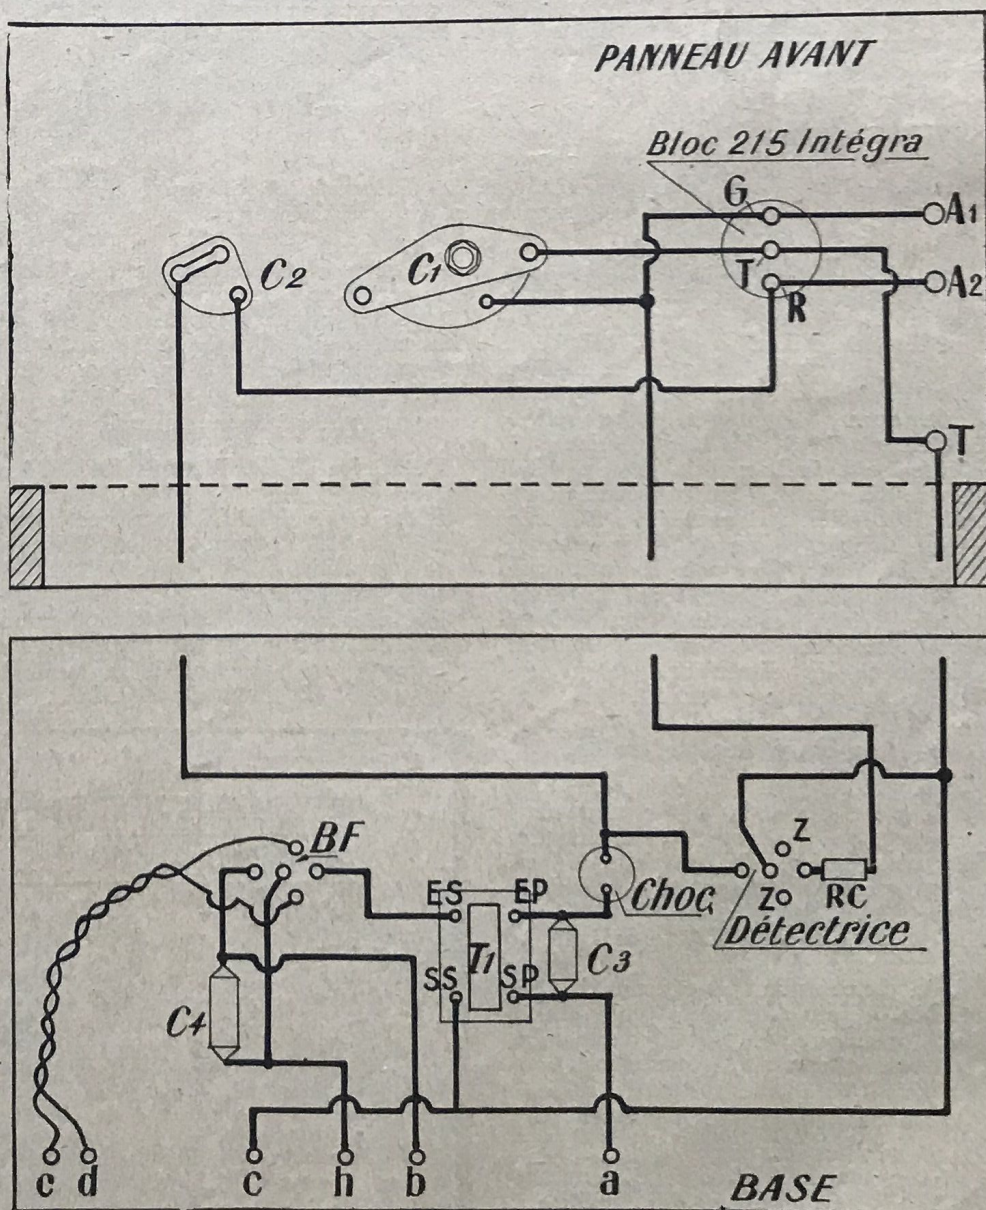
Plan de câblage du poste secteur à deux lampes (sans le dispositif d'alimentation).
